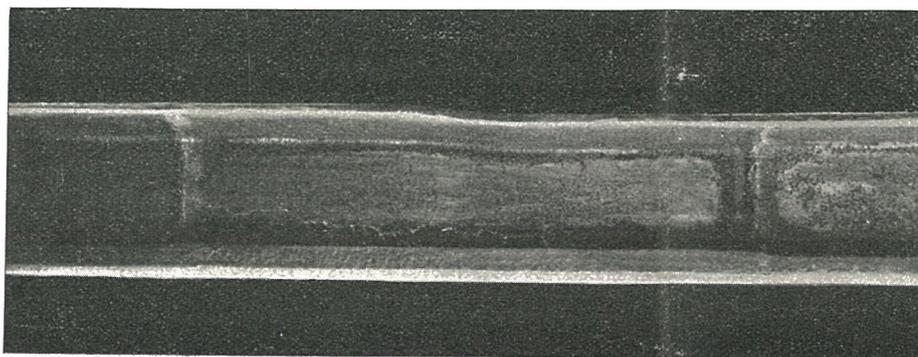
Raccord soudé pour rails de profils différents.
